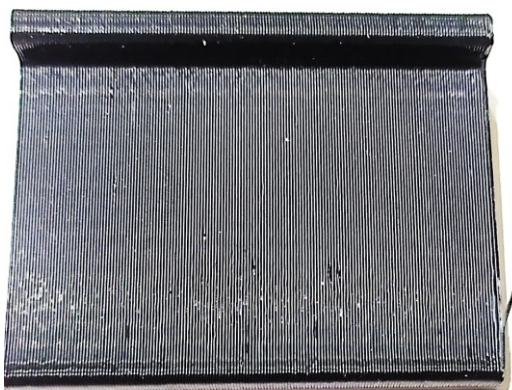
Vytisknutý koncept k otestování projevu abraze pomocí posuvného vzorku
